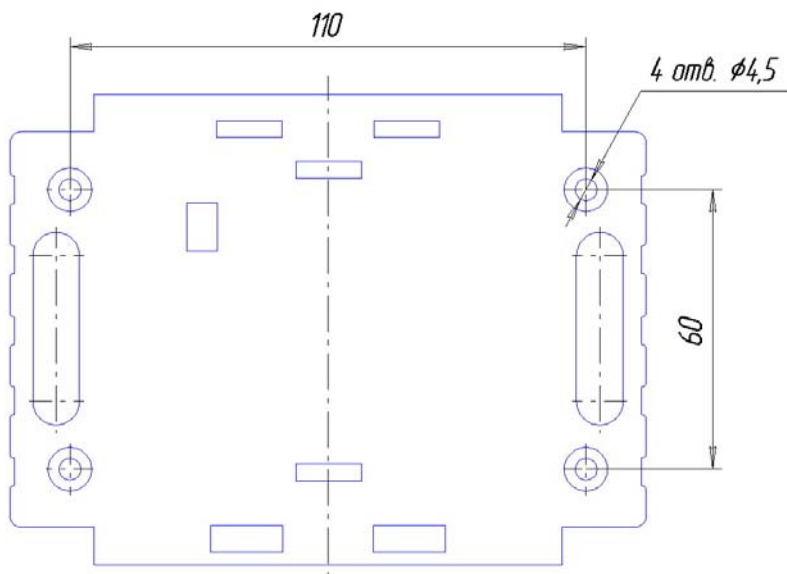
Крепление адаптера (присоединительные размеры)
